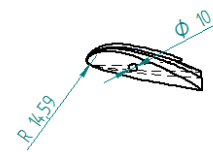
Plano Perfil NACA 2309 SOLID EDGE
